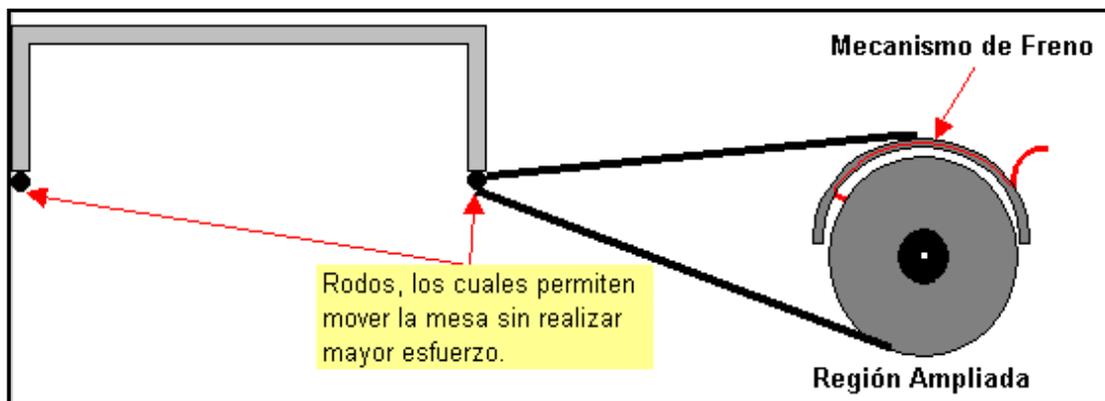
Diseño actual y propuesto para la máquina troqueladora
